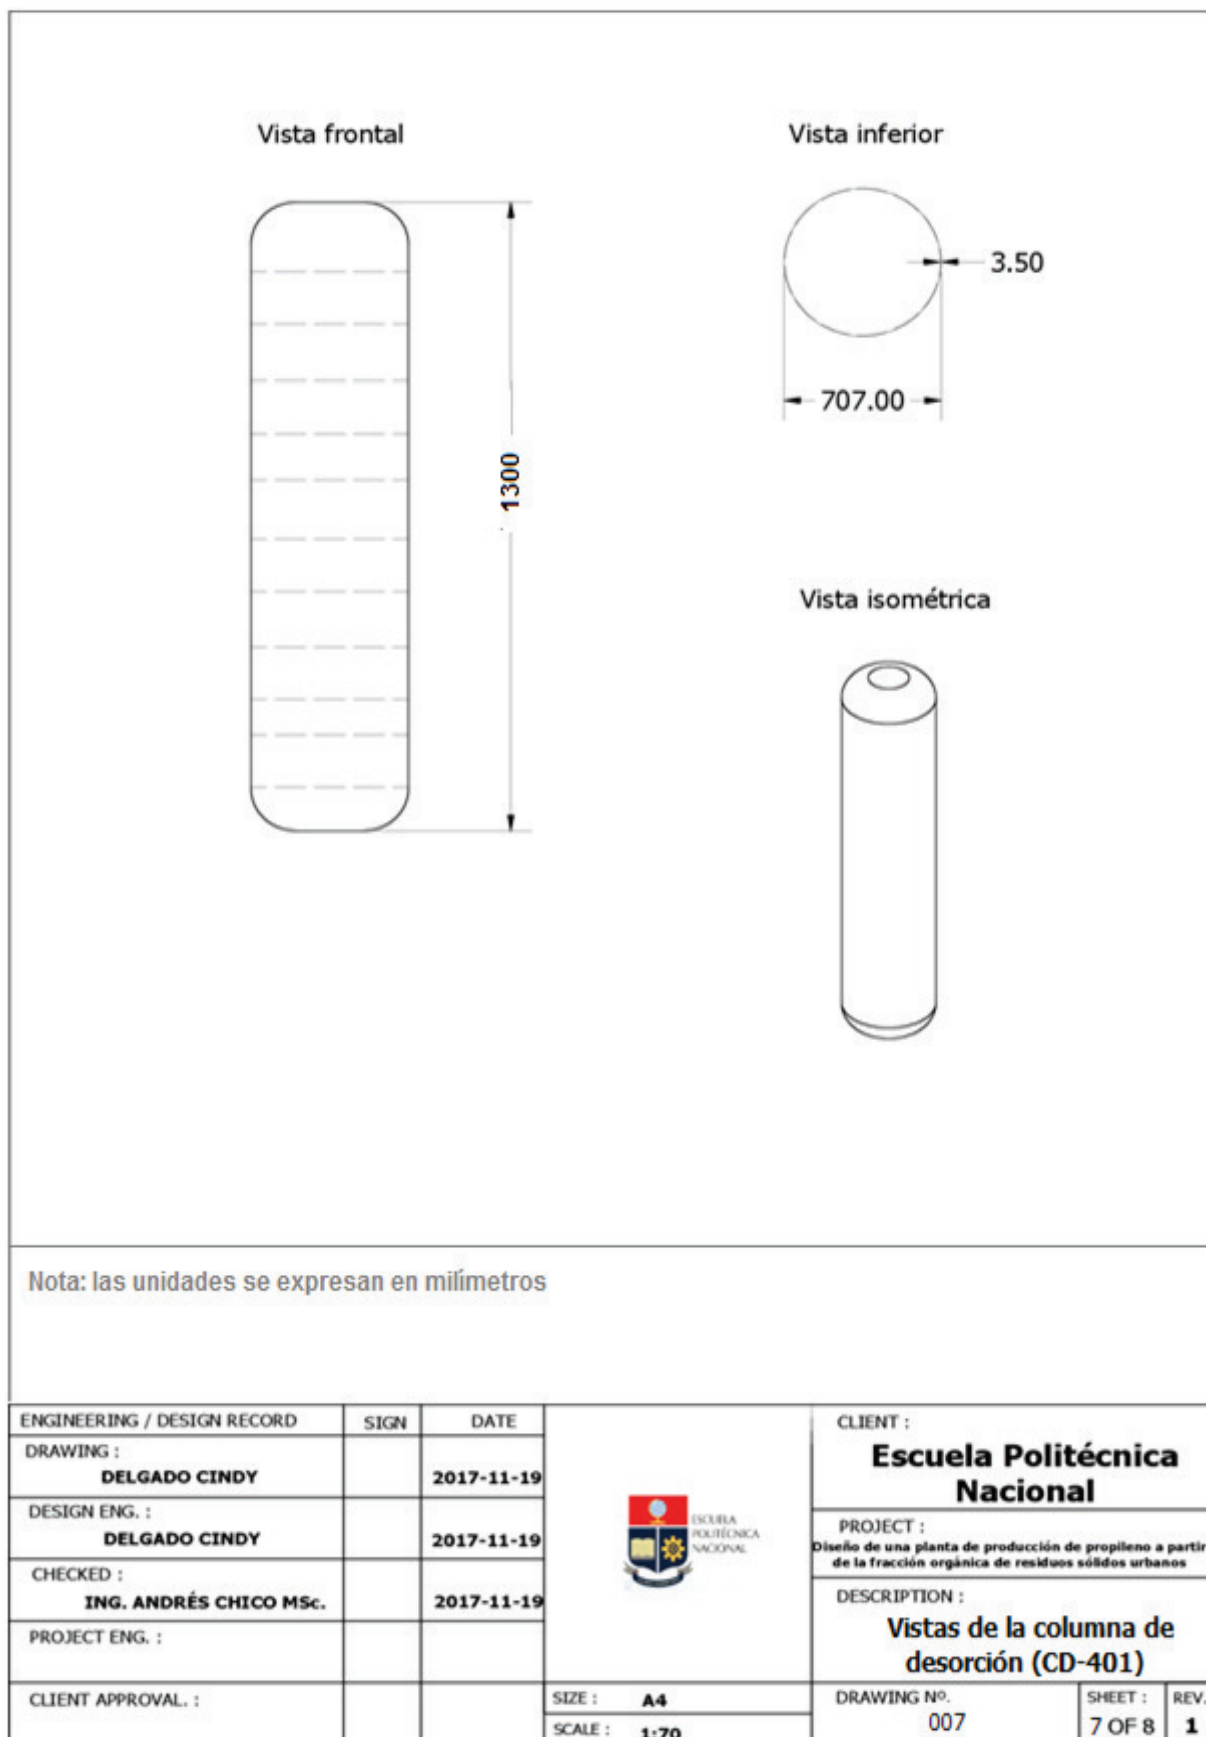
Plano de elevación de la columna de desorción (CA-401)
